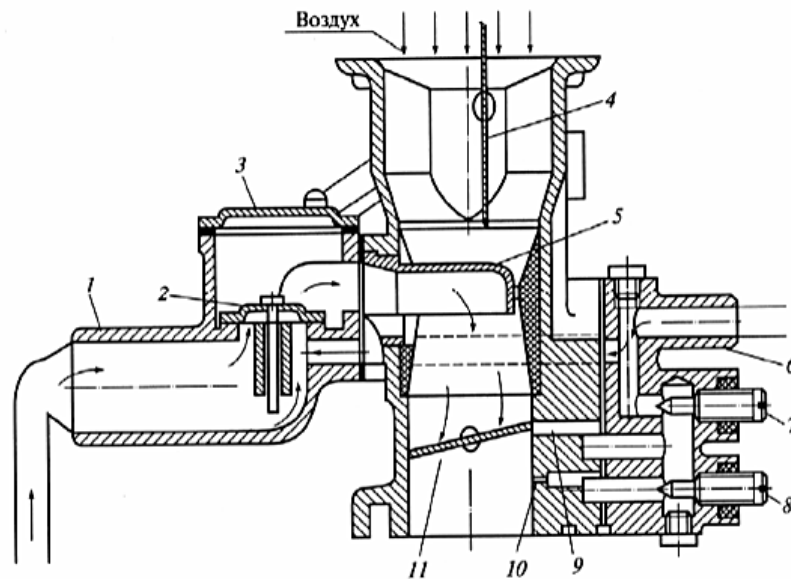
Смеситель СГ-250: 1 и 6 - патрубки подвода газа; 2 - обратный клапан; 3 - крышка; 4 - воздушная заслонка; 5- газонаполнительное устройство; 7- регулировочный винт переходных режимов; 8 - регулировочный винт системы холостого хода; 9 - канал холостого хода; 10 - канал переходного режима; 11 – дроссельная заслонка.
